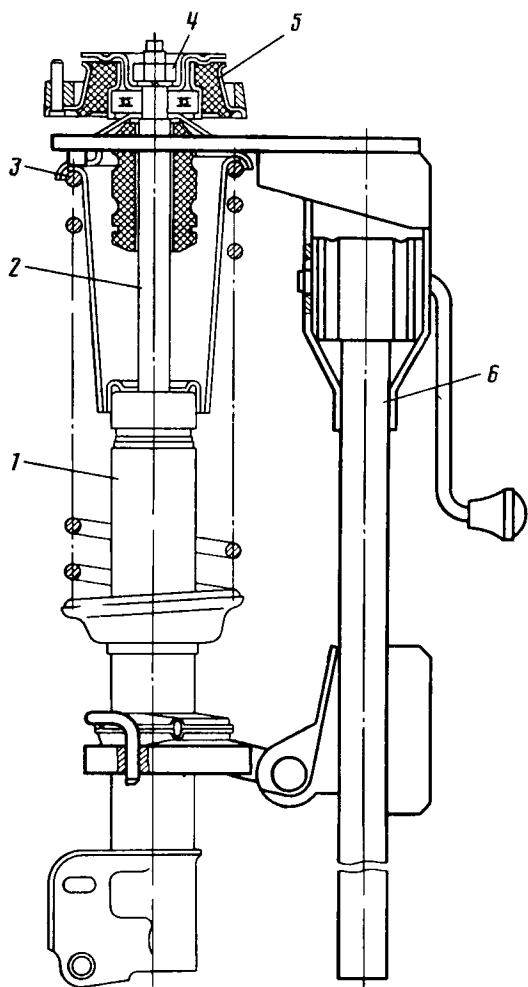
Приспособление для сборки и разборки пружины со стойкой передней подвески (вариант II, приспособлен домкрат автомобилей ВАЗ):
